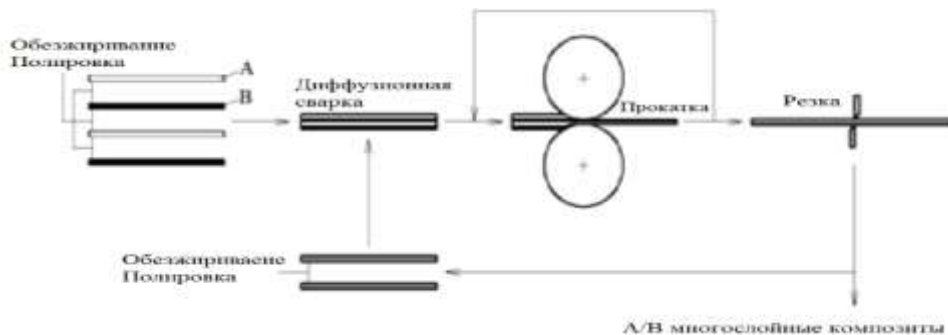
Схема повторяющегося процесса диффузионной сварки и прокатки
